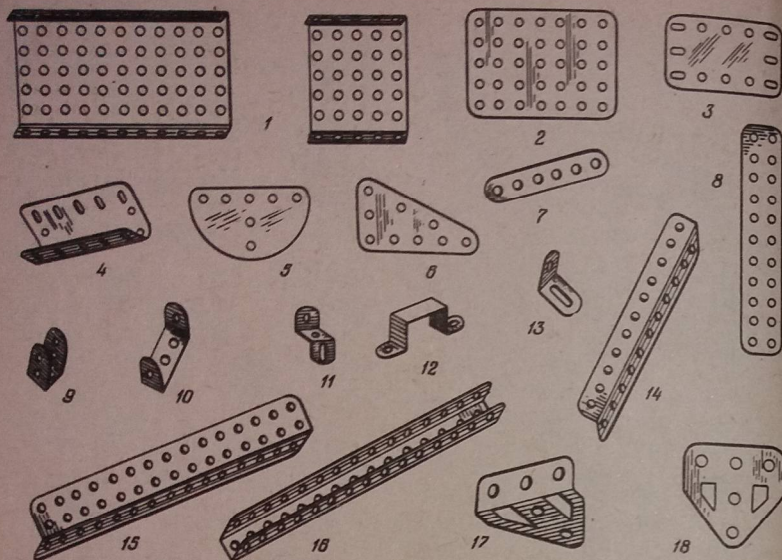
Прокатные профили: 1— плиты; 2— пластина; 3— пластина из пластика (прозрачная); 4— изогнутая пластина; 5— полукруглая пластина; 6— треугольная гибкая пластина; 7— полоса; 8— широкая полоса; 9— вилка; 10— скоба; 11— скоба с противоположно направленными уголками; 12— опора; 13— угольник; 14— равнобокий угольник; 15— неравнобокий угольник; 16— швеллер; 17— цапра; 18— цапра плоская
